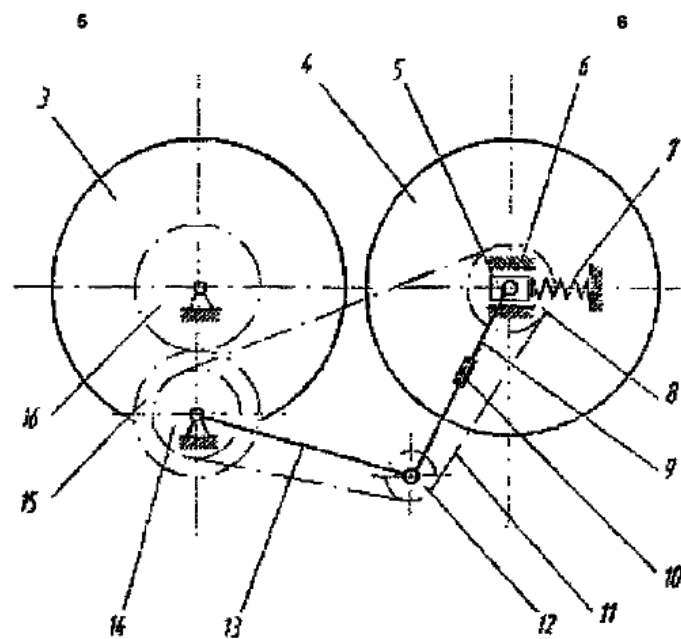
Кінематична схема передаточного механізму валкової дробарки
